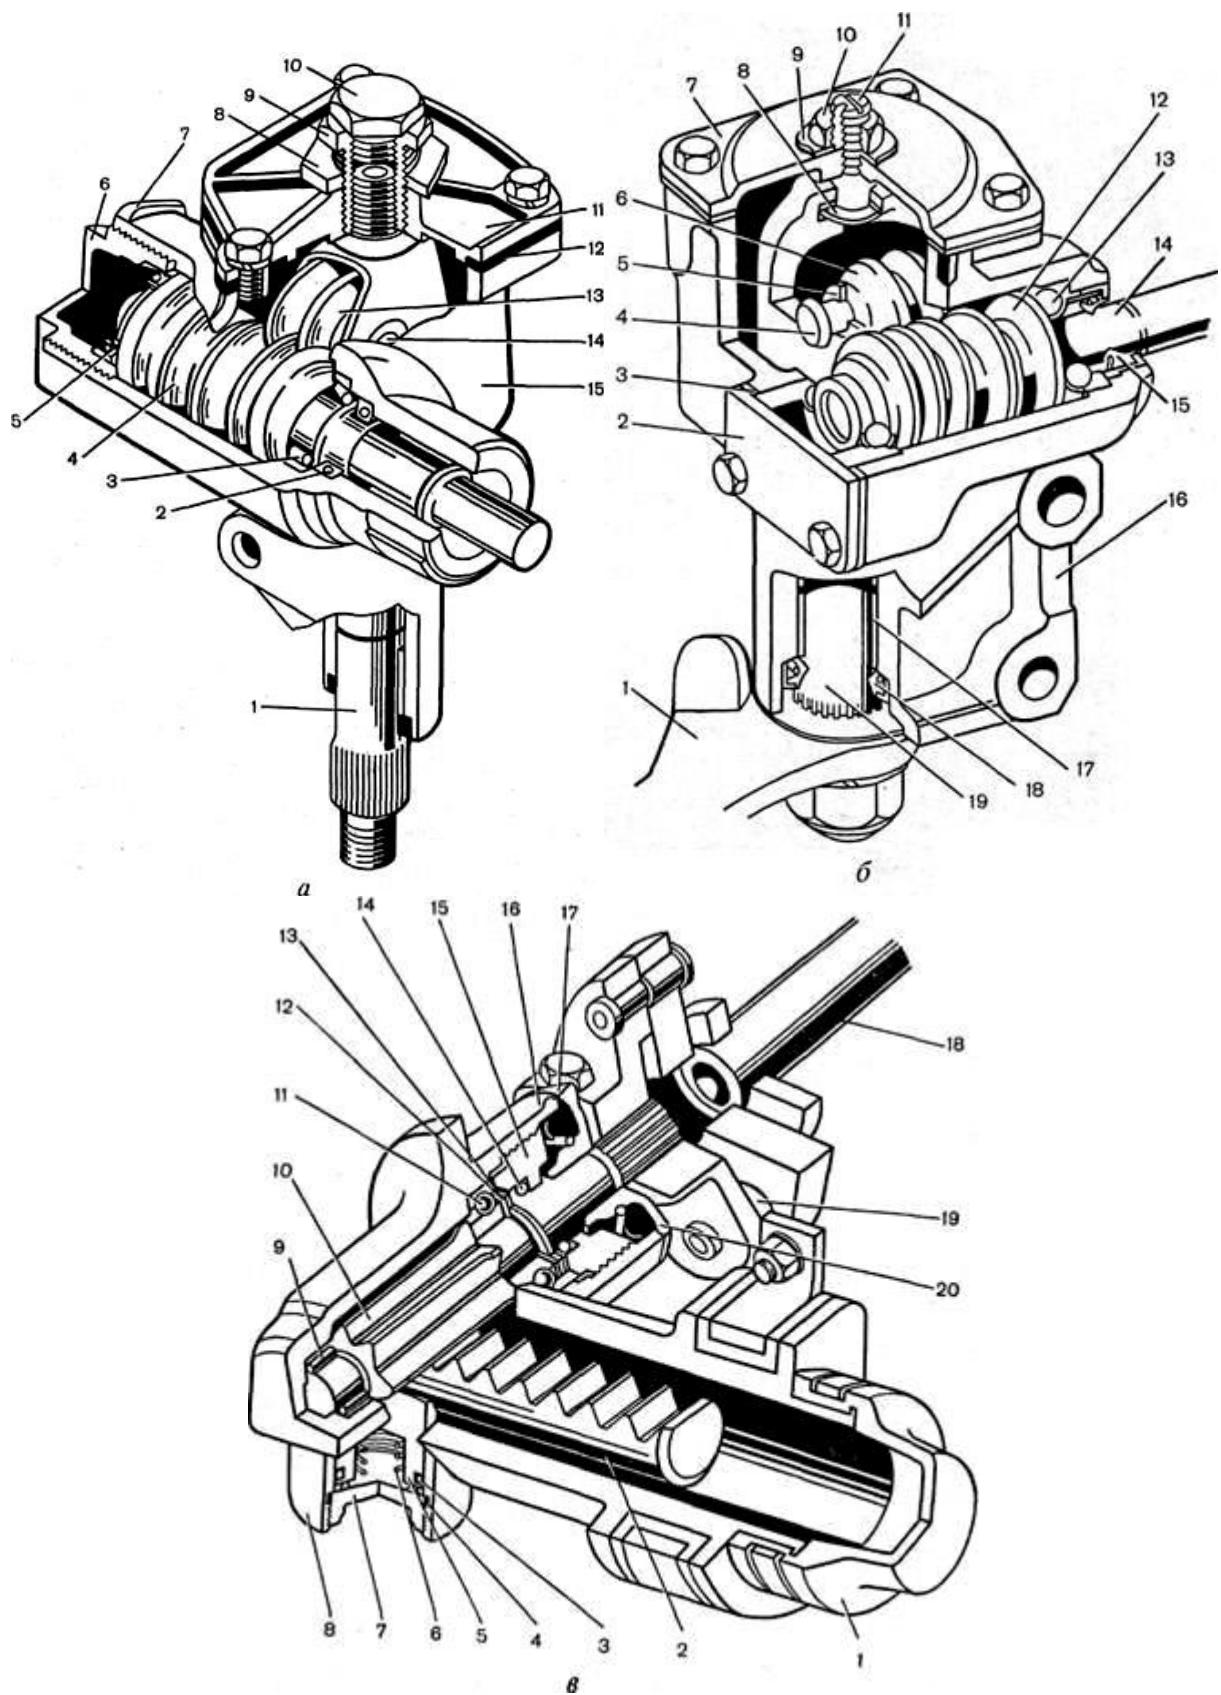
Рулевые механизмы:*a* — автомобиля ИЖ-2715: 1 — вал сошки; 2 — манжета; 3, 5 — подшипники червяка; 4 — глобоидальный червяк; 6 — регулировочная гайка подшипника червяка; 7, 8 — стопорные гайки; 9 — резьбовая втулка вала сошки; 10 — пробка наливного отверстия; 11 — крышка картера; 12 — прокладка; 13 — двухгребневый ролик; 14 — ось ролика; 15 — картер рулевого механизма; *b* — автомобиля ВАЗ-2121: 1 — рулевая сошка; 2 — крышка нижняя; 3 — регулировочные
